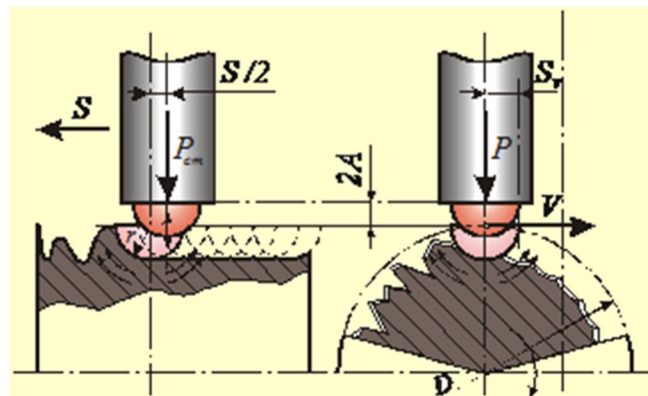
Схема поверхнево пластичного деформування при ультразвуковій зміцнюючій обробці
